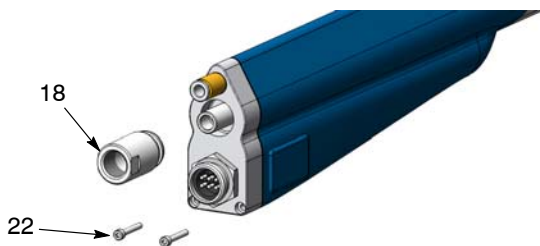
Dépose du dissipateur thermique et de l'écrou de blocage
